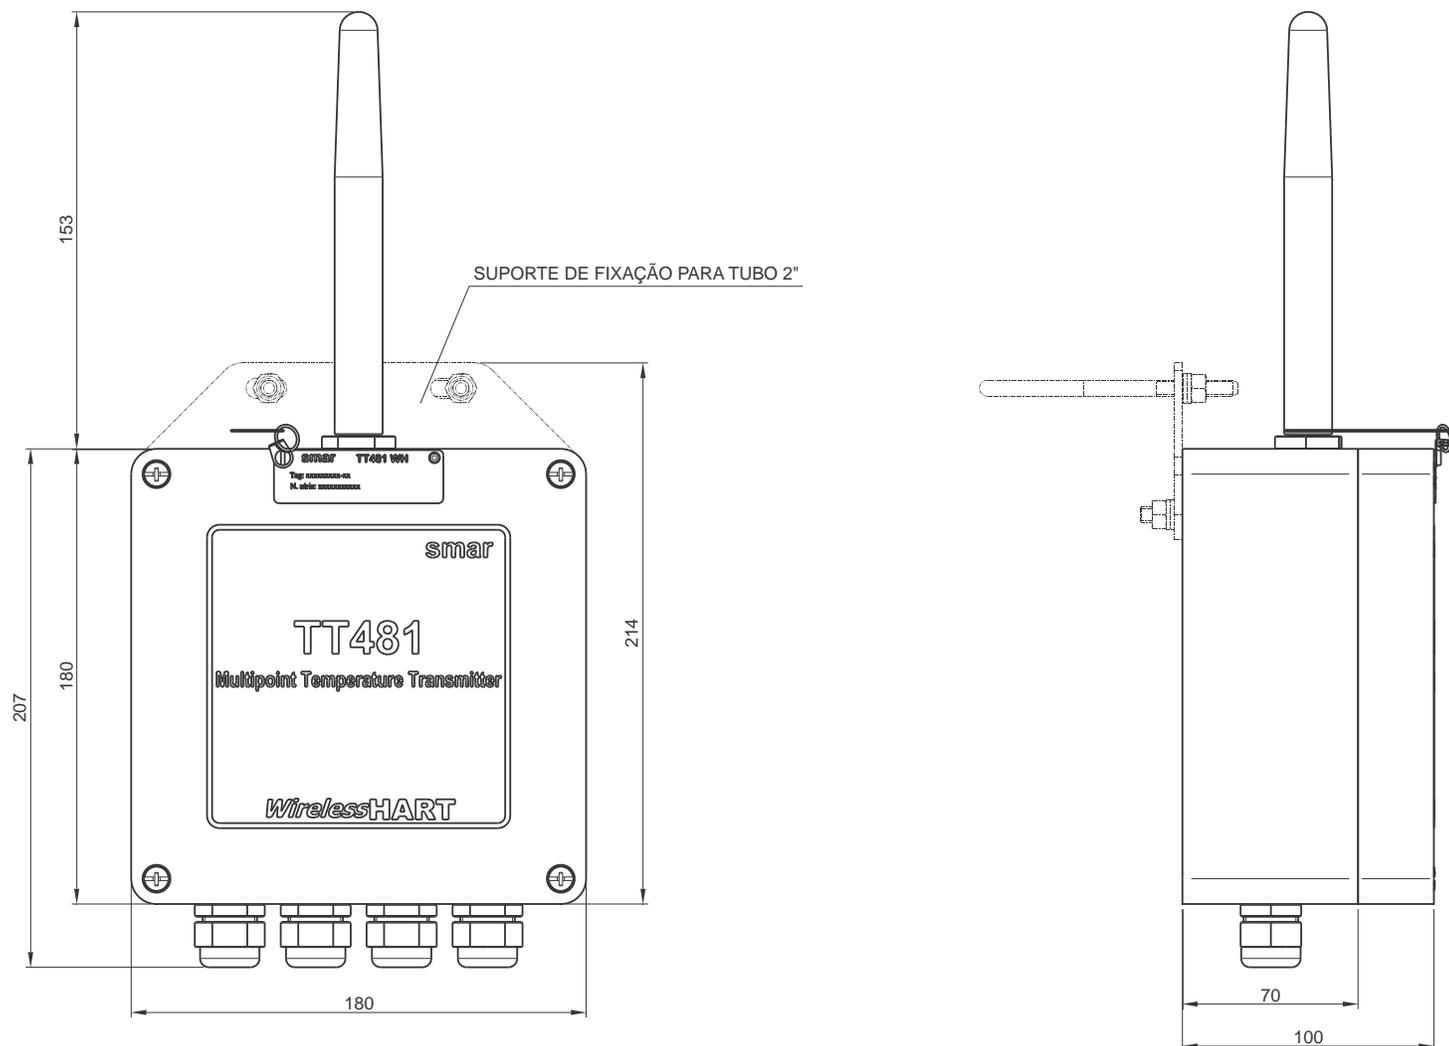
(a) - Desenho Dimensional - TT481 WirelessHART™ com 4 Canais
